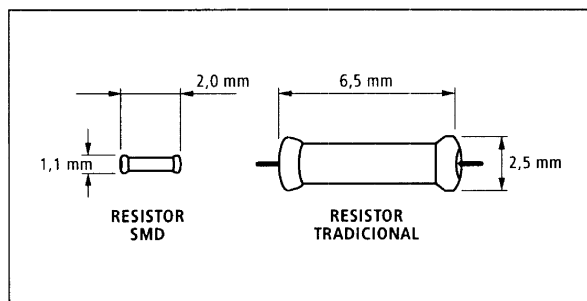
Dimensões principais de dois resistores: SMD e Tradicional.
